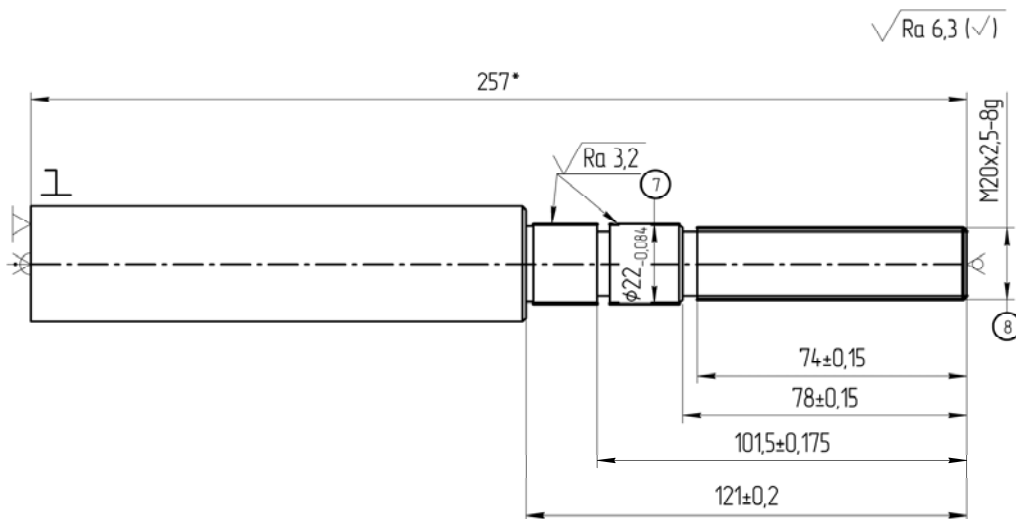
Эскиз токарной чистовой обработки вала (чистовое точение шеек, нарезание резьбы)
